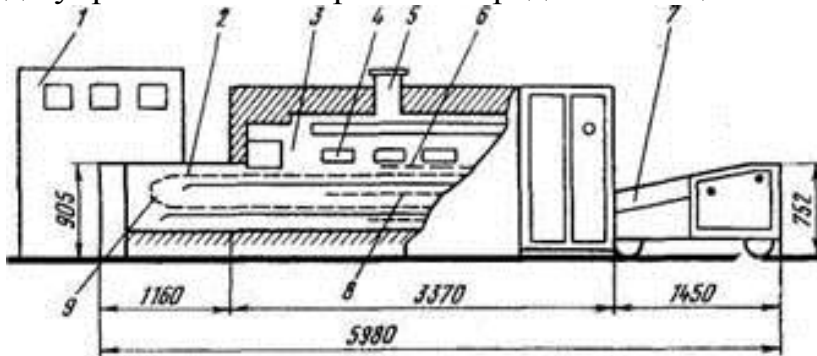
Схема печі конструкції Брувера – Саліхова для випічки середньоазіатських коржів
